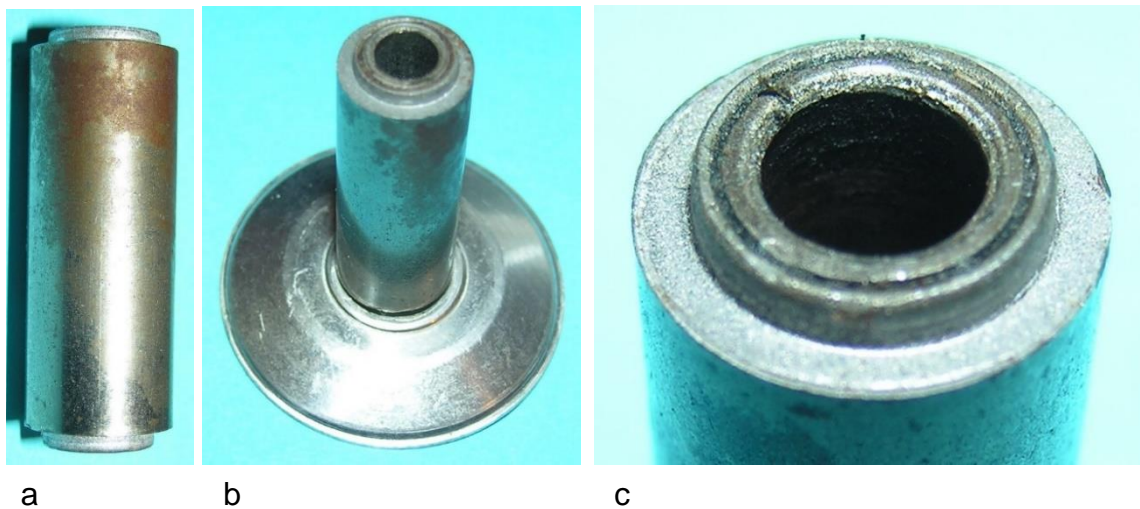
Stahlsinterlager: a) Lagerrohr mit 3 mm Wandstärke und 30 mm Länge, b) Lagerrohr mit Lagerschild, c) Abgesetzte Stirnseite
